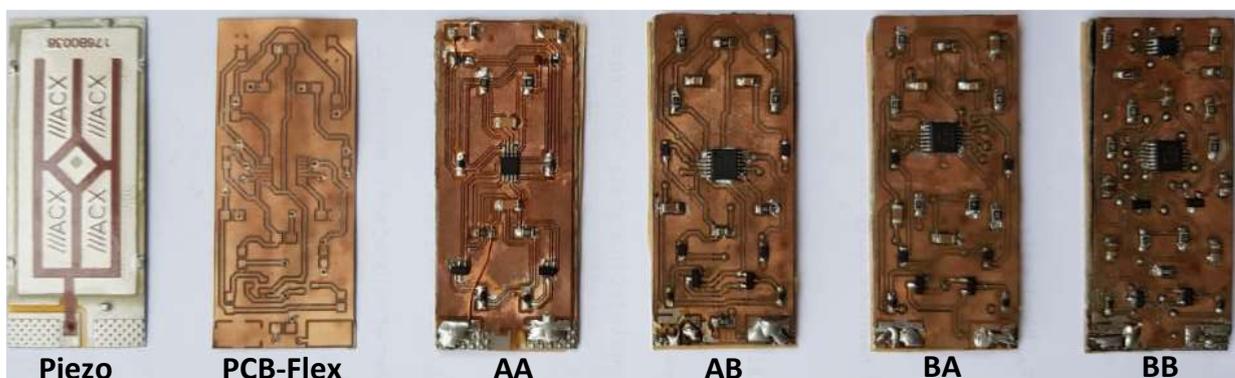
Piezo, placa PCB-Flex e protótipos construídos e já soldados.
